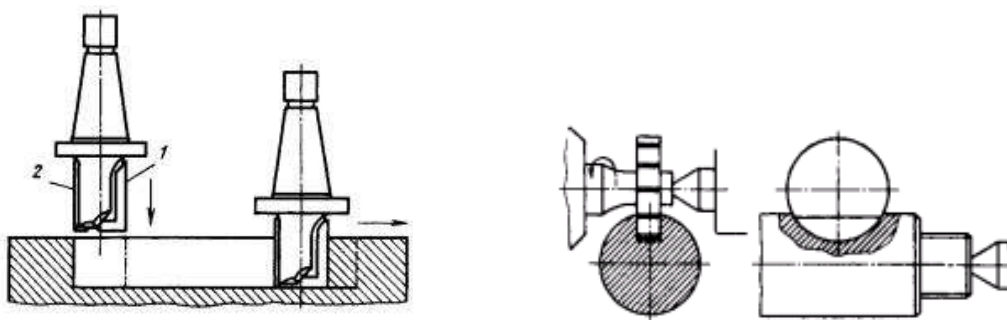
Обработка шпоночных пазов сверлопазовой фрезой Walter и шпоночного паза под сегментную шпонку дисковой фрезой
